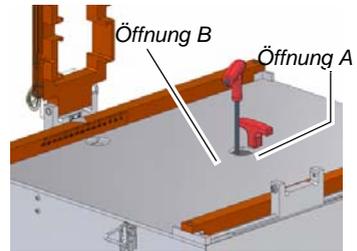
Stecken Sie den T-Schlüssel in Öffnung A, lösen Sie mit Sechskantschlüssel die Bolzen in B
